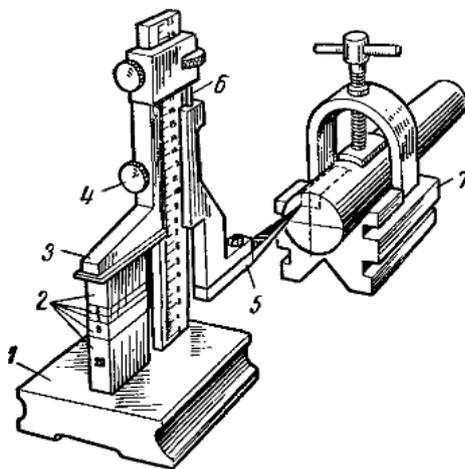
Разметка шпоночной канавки с применением плоскопараллельных концевых мер длины (плиток): 1 — измерительная поверхность, 2 — блок плиток, 3 — измерительная ножка, 4 — зажимный винт, 5 — чертилка, 6 — микрометрический винт, 7 — призма
